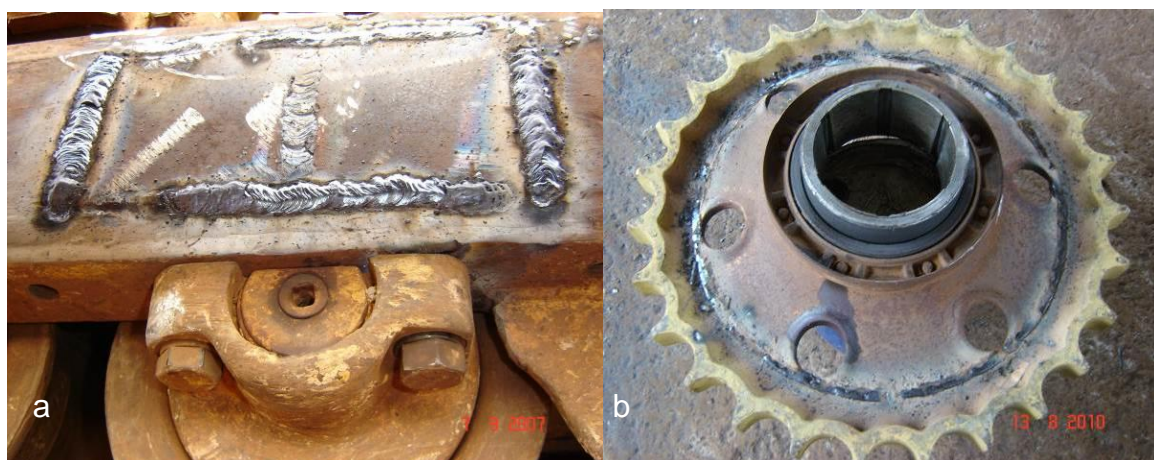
a) Soldagem de estrutura lateral do truque (suporte de rolete); b) Soldagem do aro motriz direita).
